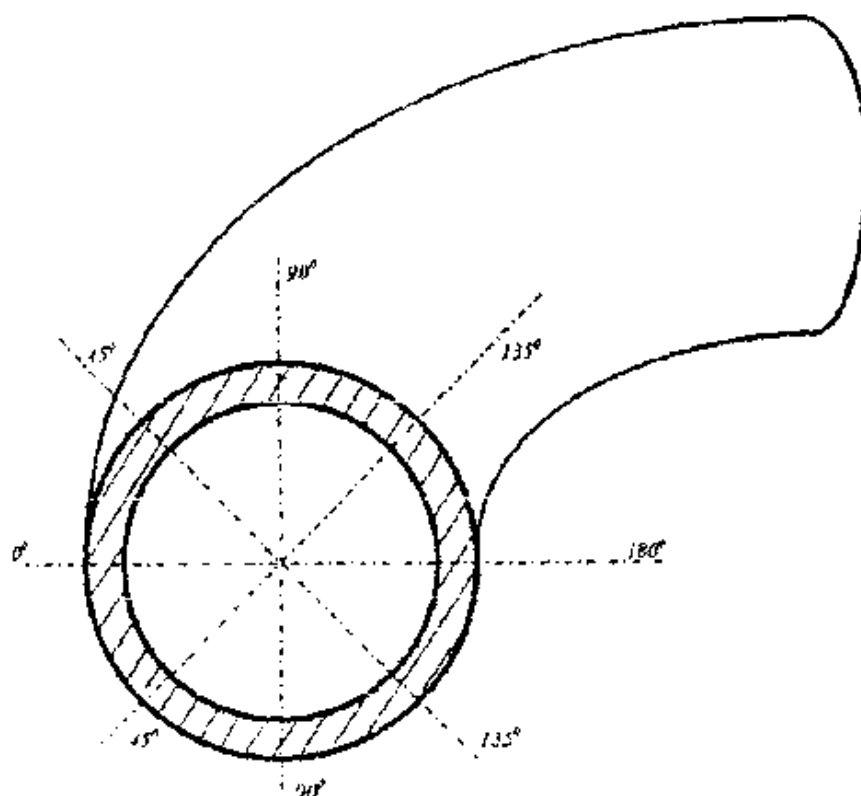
Углы расположения сварного шва относительно плоскостигиба
